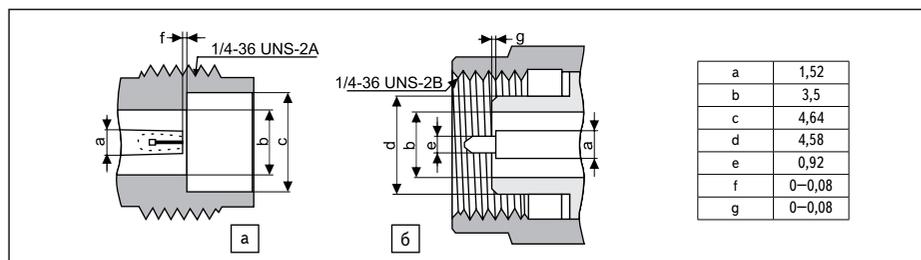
Интерфейс 3,5-мм соединителя: а) розетка; б) вилка
